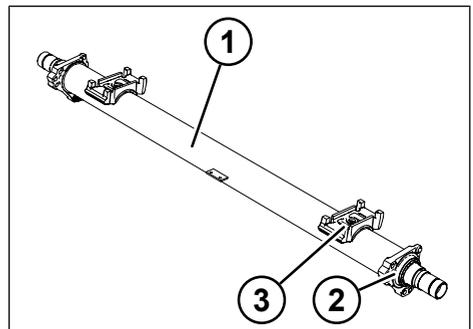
Bauteile des Achskörpers (Luftfederlenker oben)
